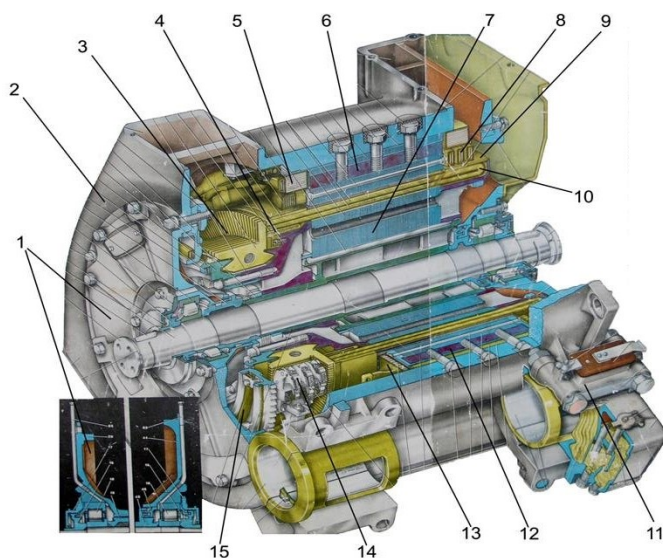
Підшипникові корпуси (щити) із роликовими підшипниками тягового двигуна НБ-418К
